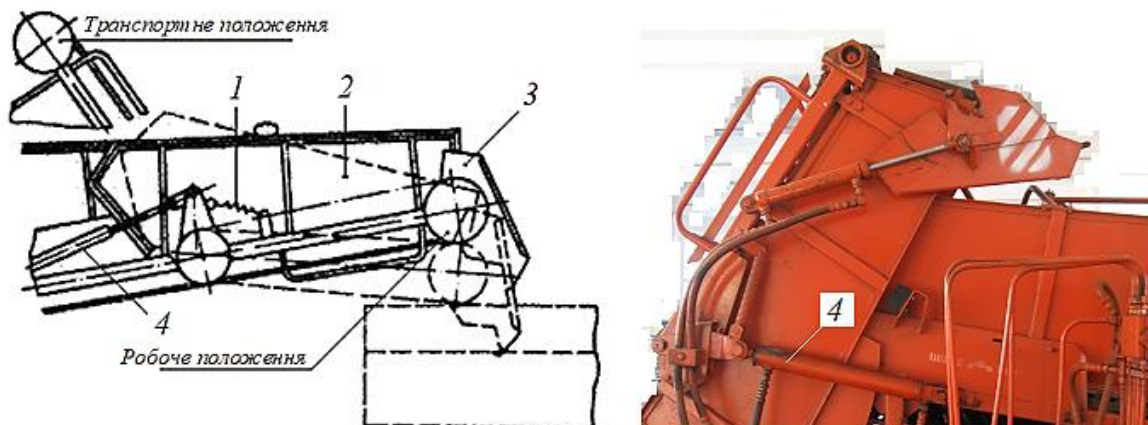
Регулювання розташування відкидної частини бункера: 1 - пружина; 2 - рухома частина бункера; 3 - лоток; 4 - гідроциліндр
